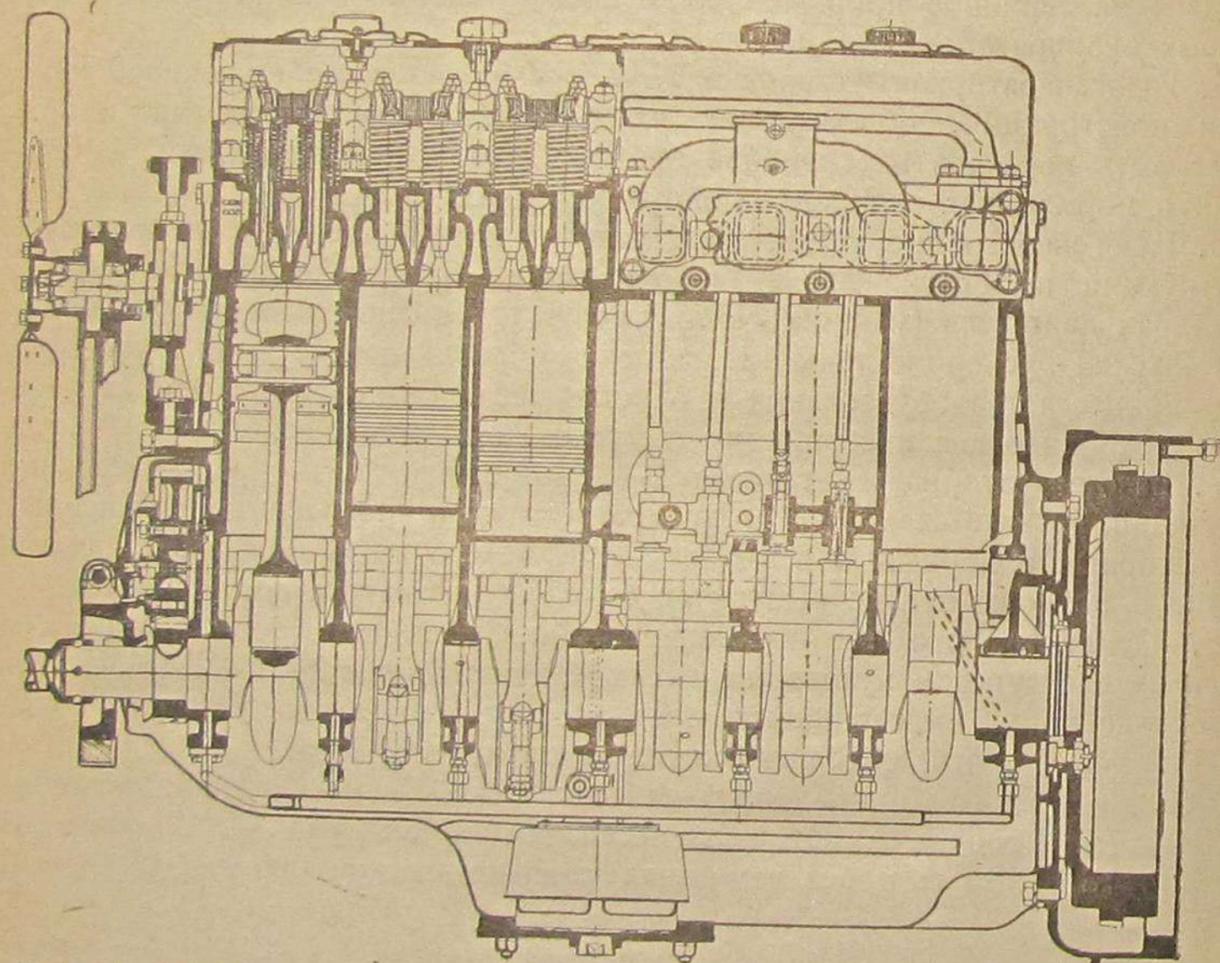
Продольный разрез двигателя НАТИ М-12.
